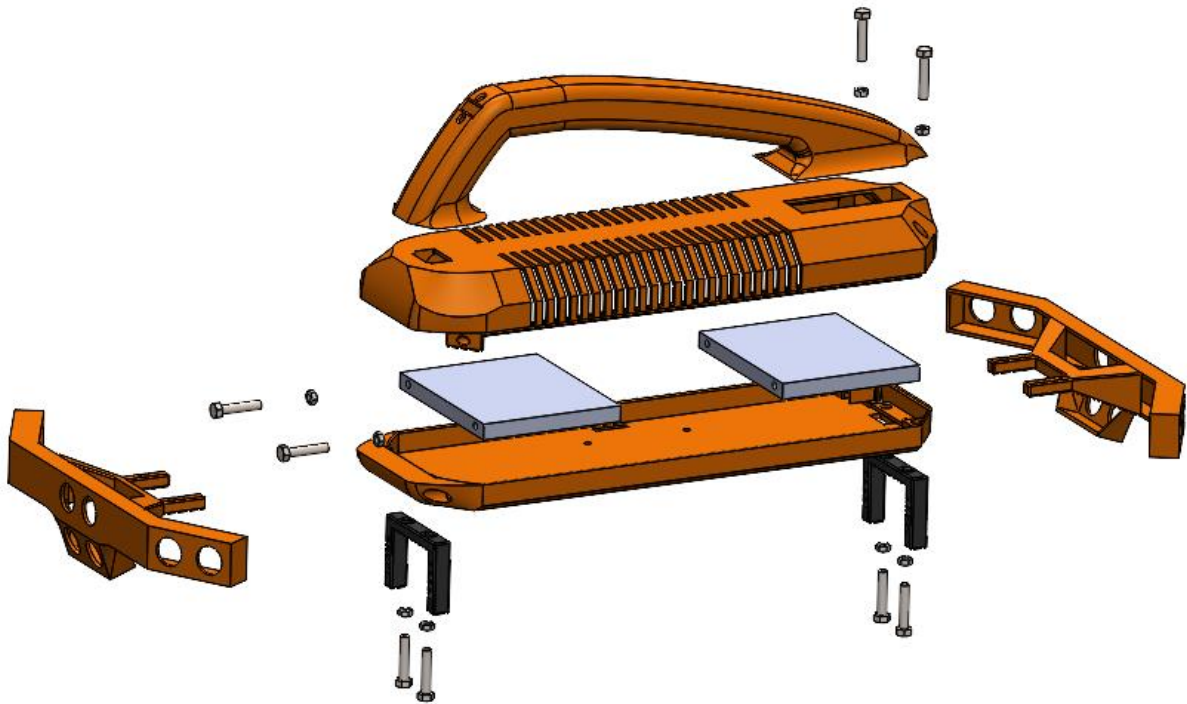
Vista Explodida da montagem completa do suporte principal e seus fixadores.
